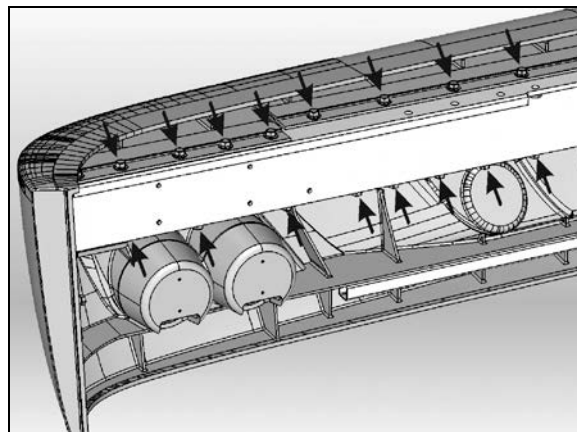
PIÈCES EXTRUDÉES EN ALUMINIUM – DÉMONTAGE DE L'HABILLAGE DU PARE-CHOCS
